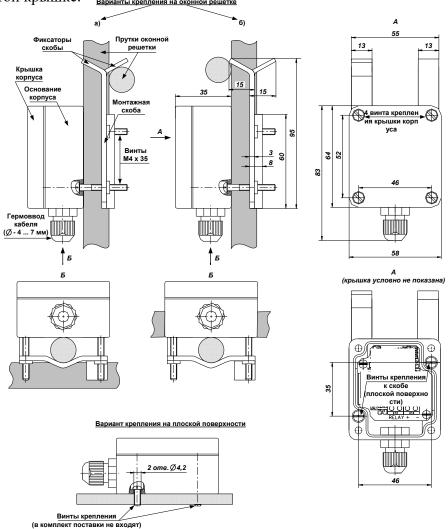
Внешний вид, варианты крепления, габаритные и установочные размеры.
